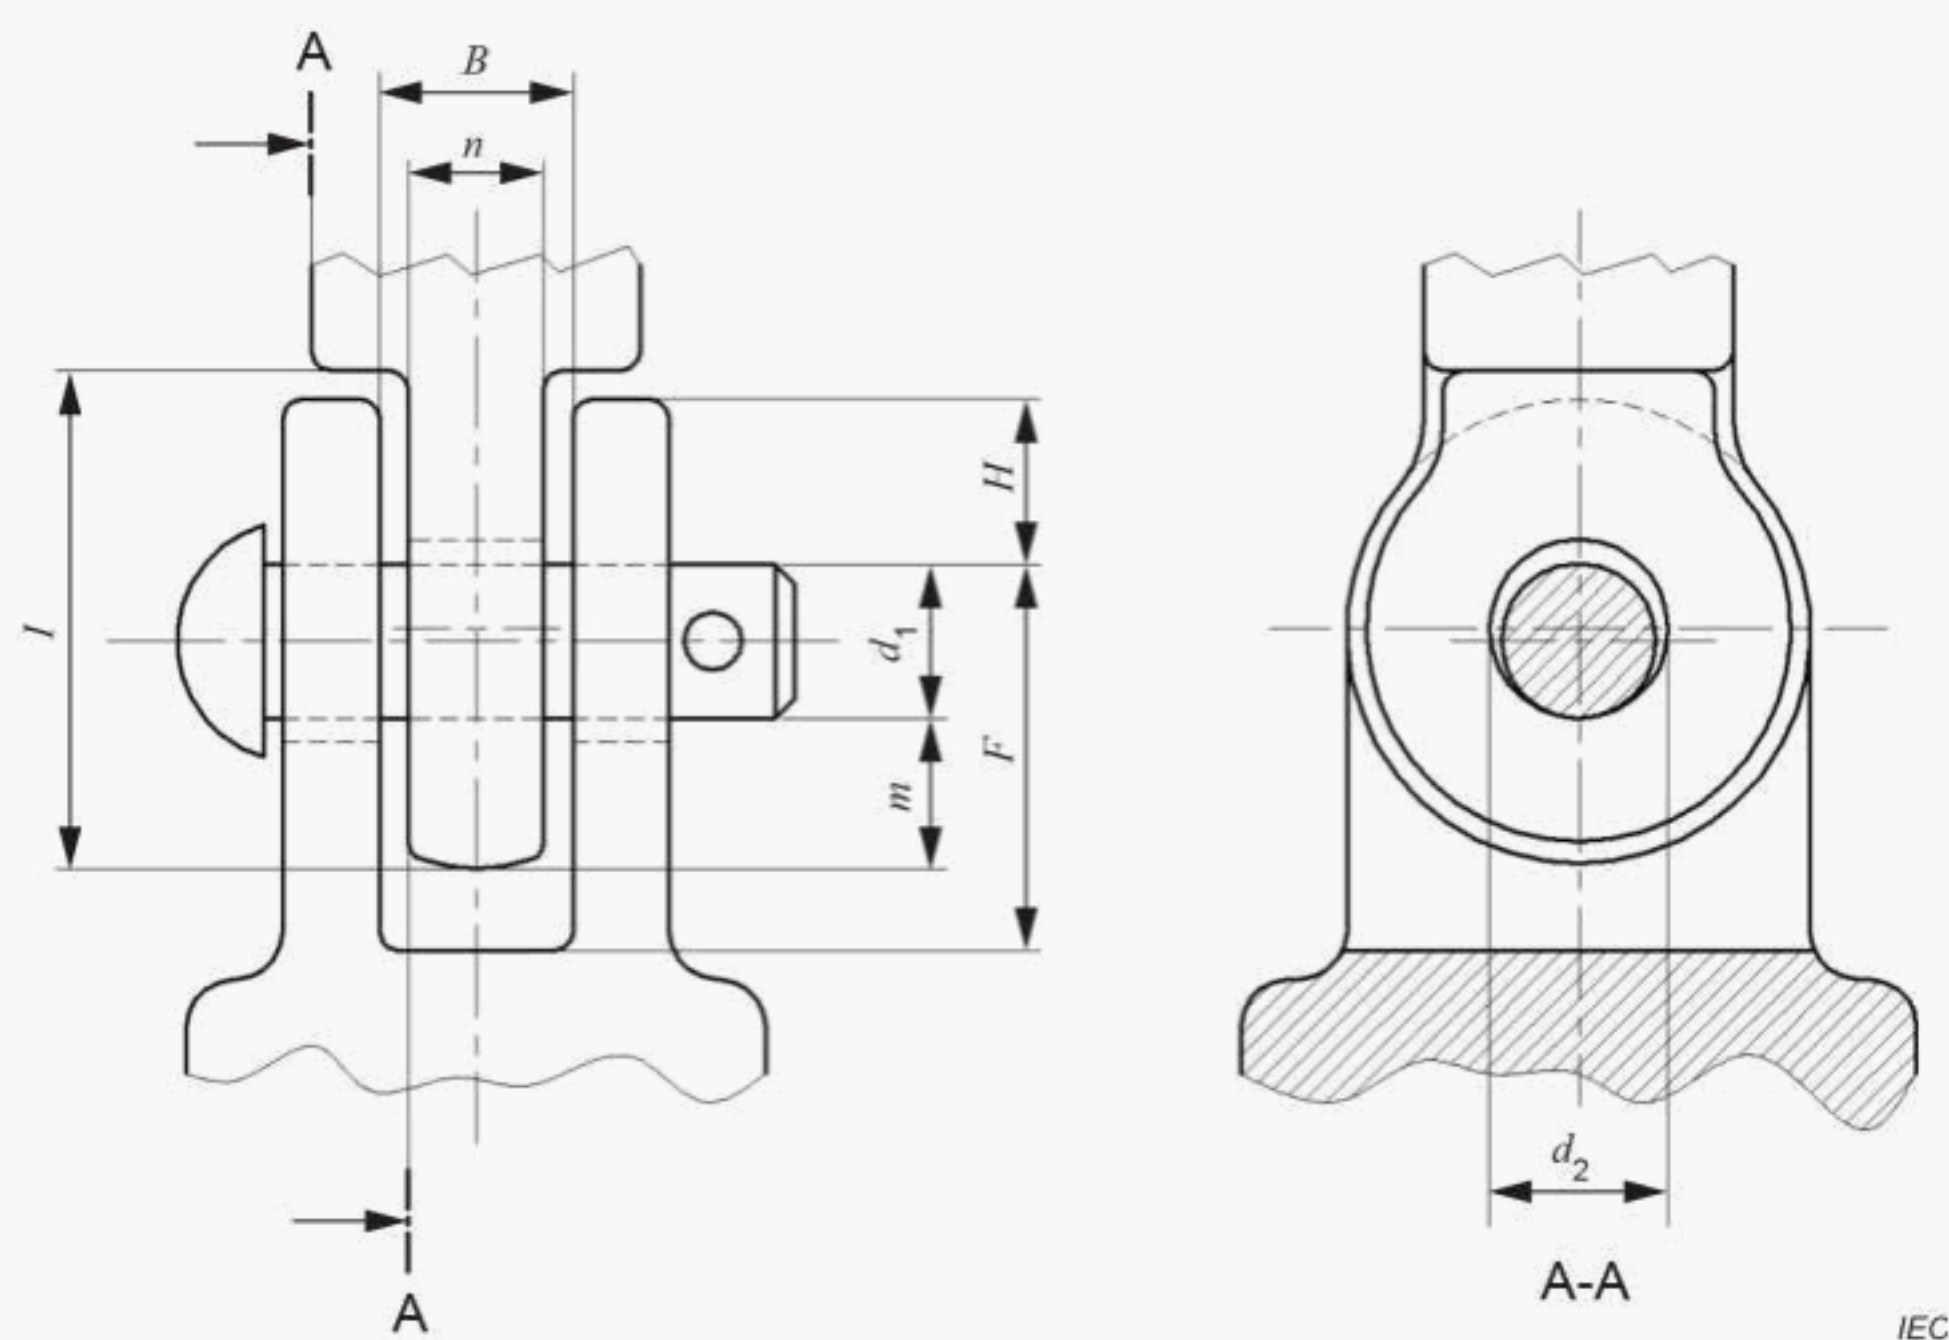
Dimensions des assemblages à chape et tenon pour les isolateurs à long fût
